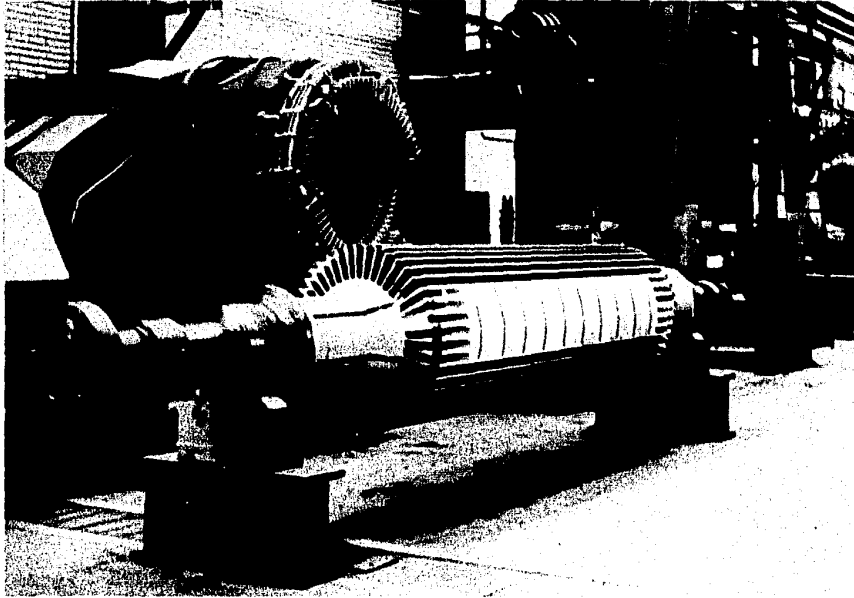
ROTOR MAQUINADO LISTO PARA COLOCARSE EN EL DEVANADO.
